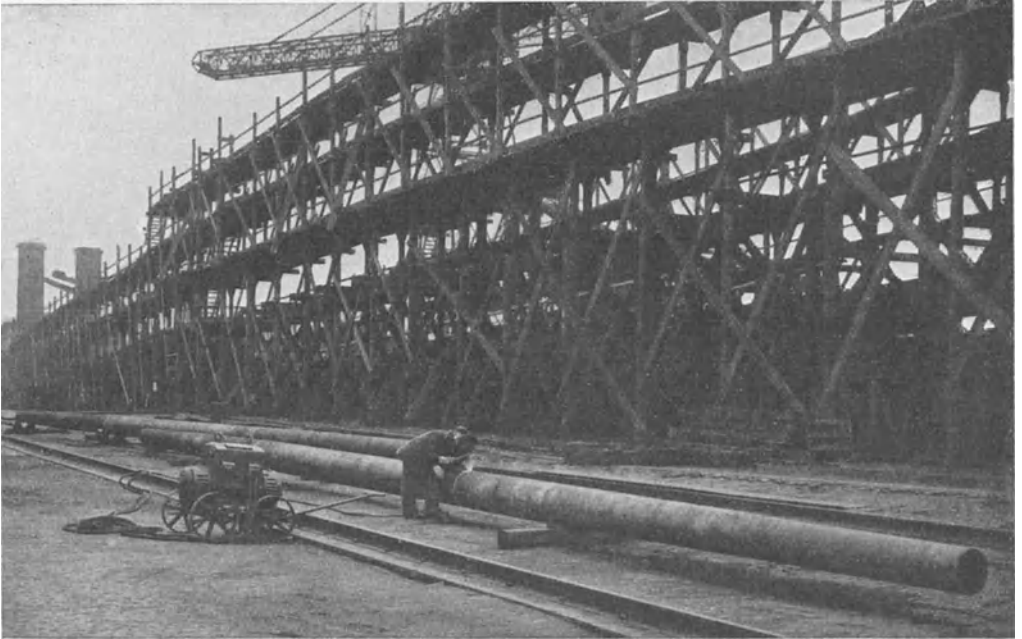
Schweißung eines Schiffsmastes.
